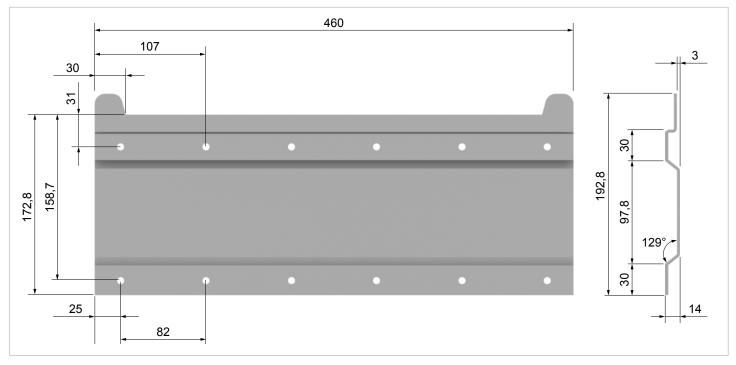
Dimensions de la plaque de montage (en mm)
